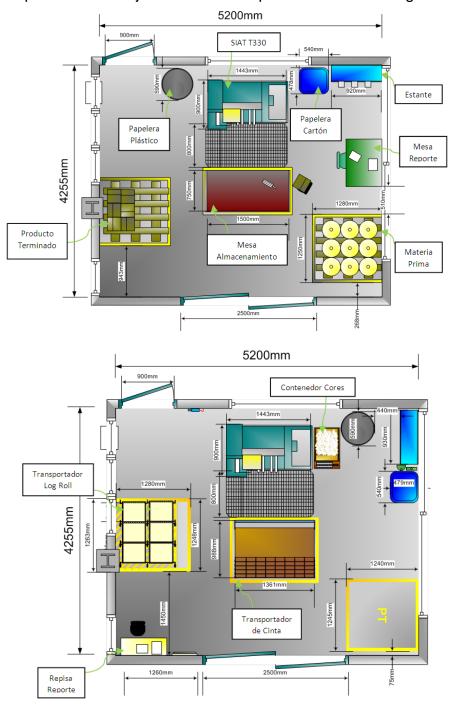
Distribución en planta actual y propuesta del área de corte de cinta.
